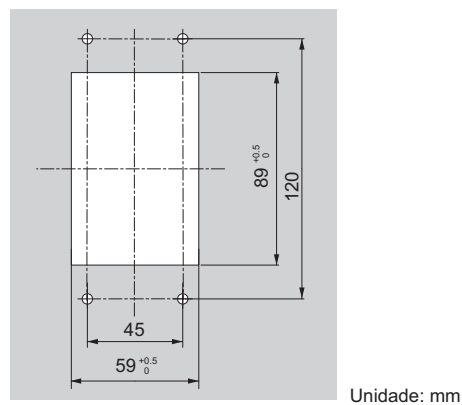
Dimensões de corte do painel (instalação de montagem interna/embutida)
